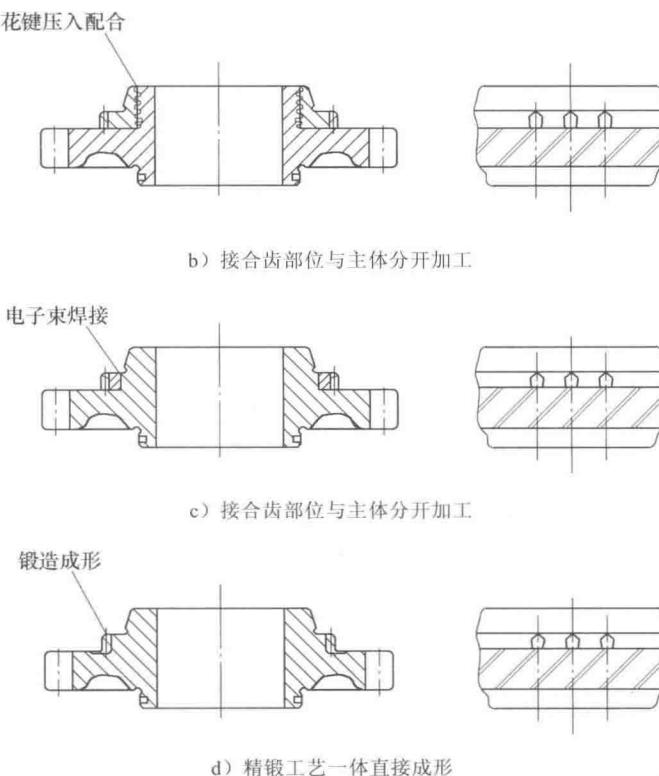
汽车变速器同步器接合齿轮的加工方法 (续)
